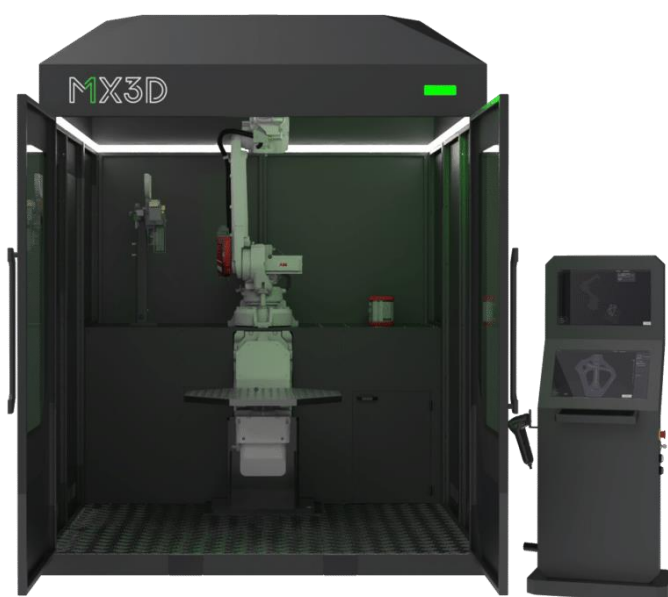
Гібридний 3D принтер від M1 System Industrial 3D Printing Robotics
